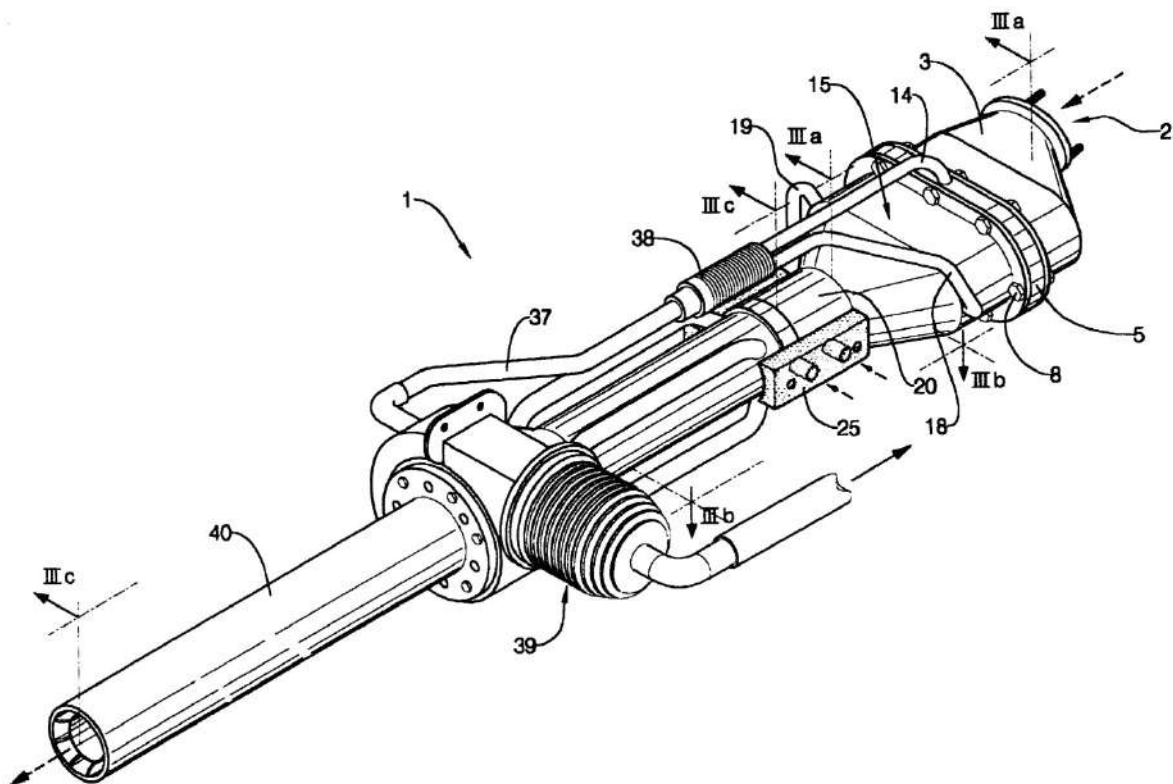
Загальний вигляд пристрою для очищення вихлопних газів
